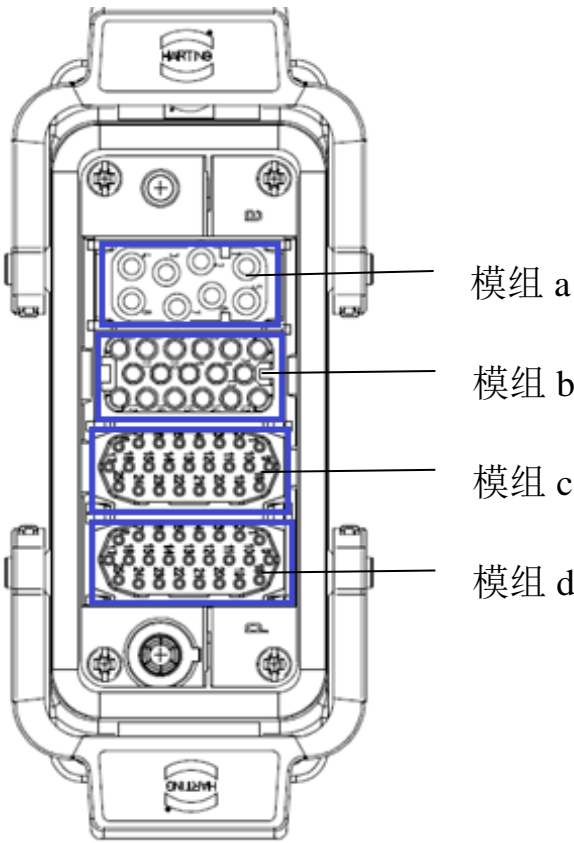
GTSD64 6KW MOTOR 重载连接器外观图
